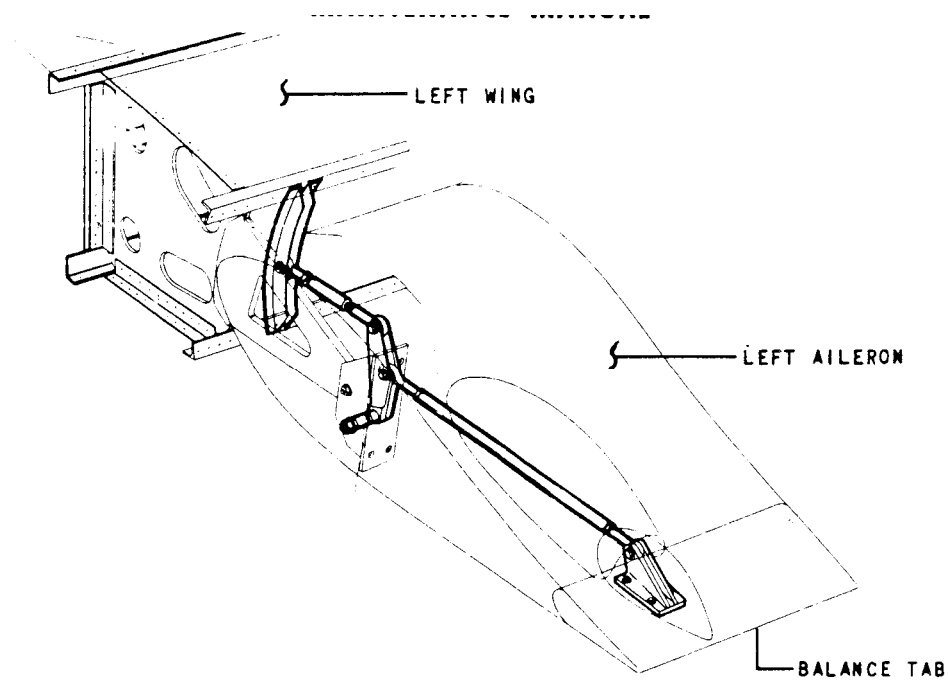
Mecanismo Actuador del Balance-Trim tab
